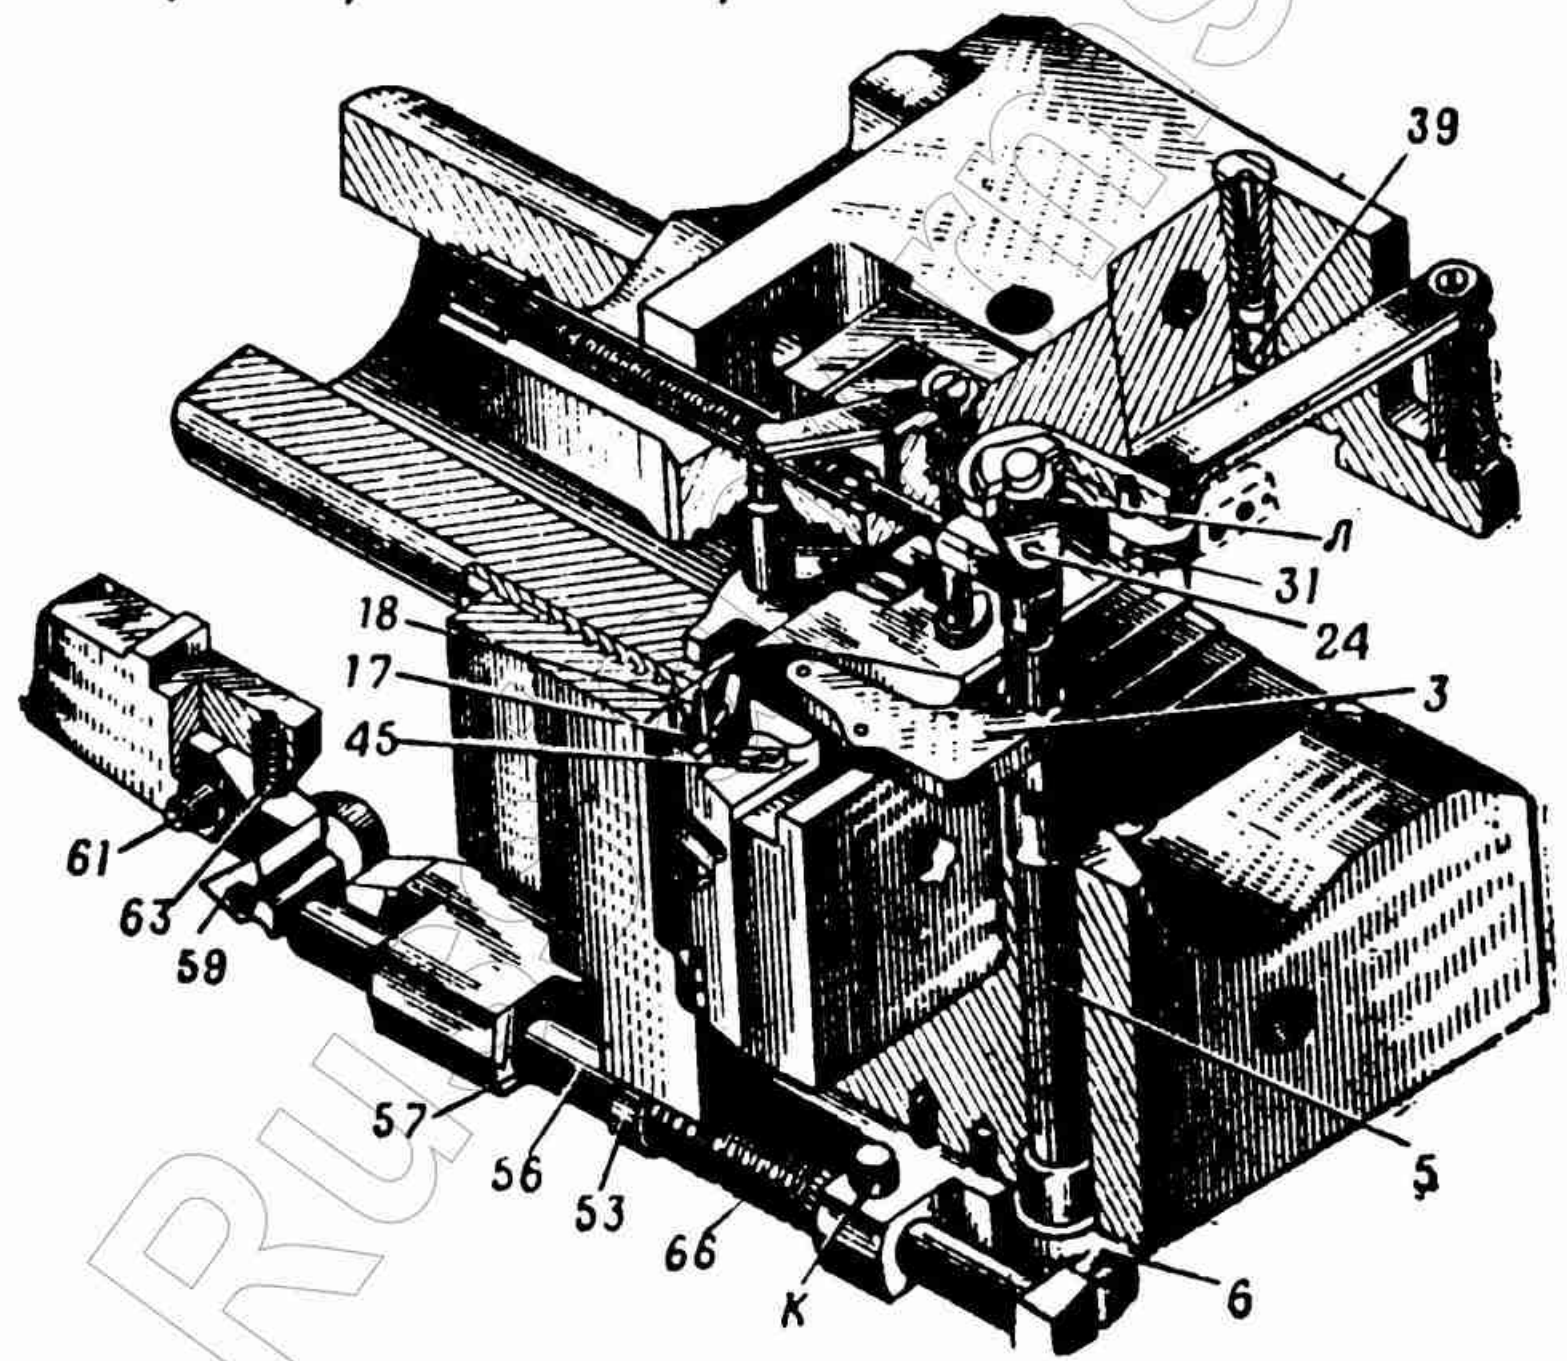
Затвор Д10-ТГ и Д10-Т2С в собранном виде (расположение деталей на 1 — клин; 2 — рукоятка затвора; 3 — кривошип с роликом; 5 — ось кривошипа; 6 — кулачок по нижний выбрасыватель; 23 — ось выбрасывателя; 24 — рычаг закрывающего механизма; 27 — щелка рукоятки; 39 — стопор упора; 45 — ось предохранителя спуска; 53 — кольцо; 56 — скалка; ограничитель рукоятки; 80 — ось повторного взвода;
